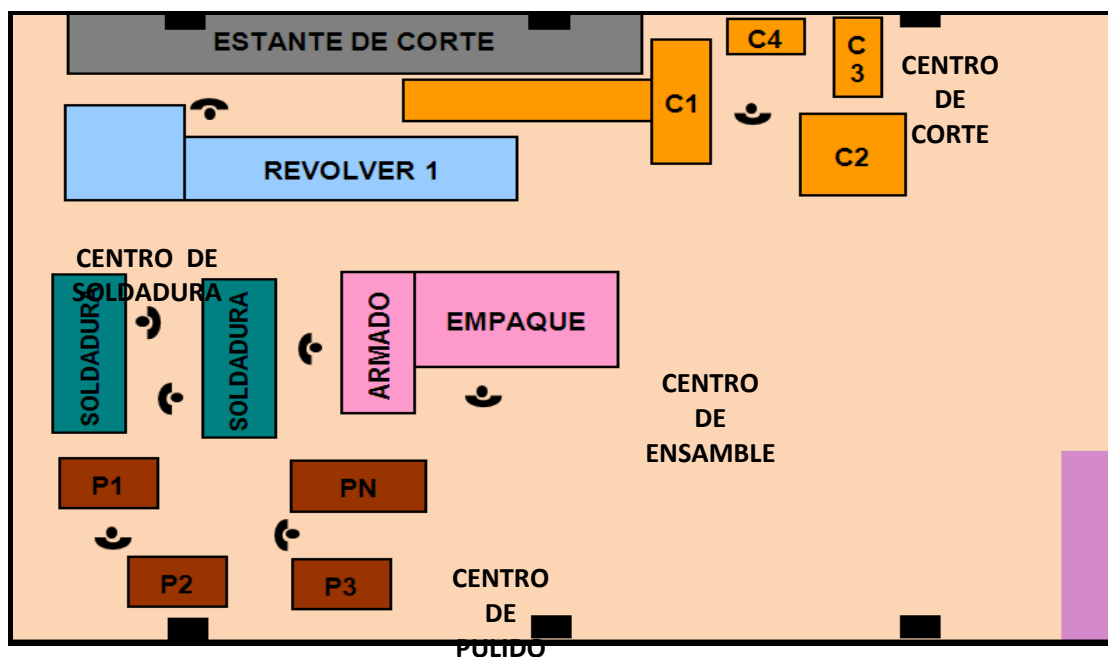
Zoom 1 de la parte derecha de la planta.
